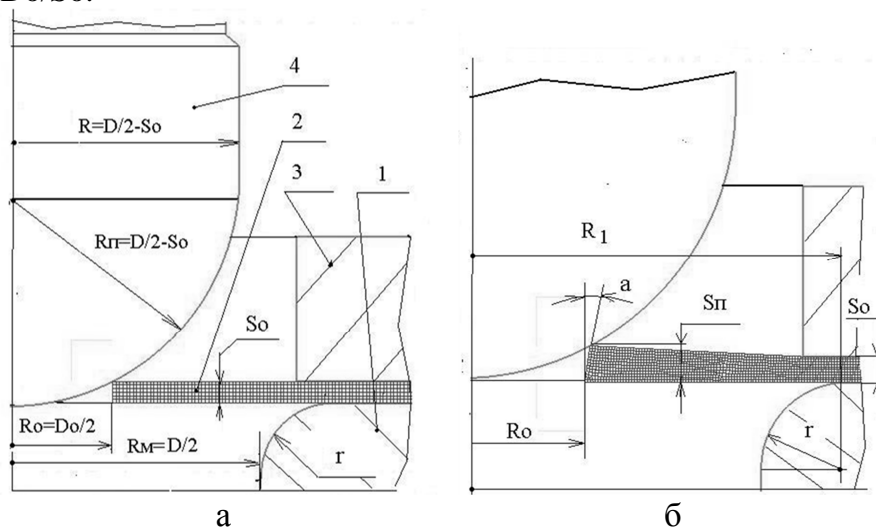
Розрахункова схема відборткування: а – відборткування традиційної заготовки, б – відборткування зпрофільованої заготовки
